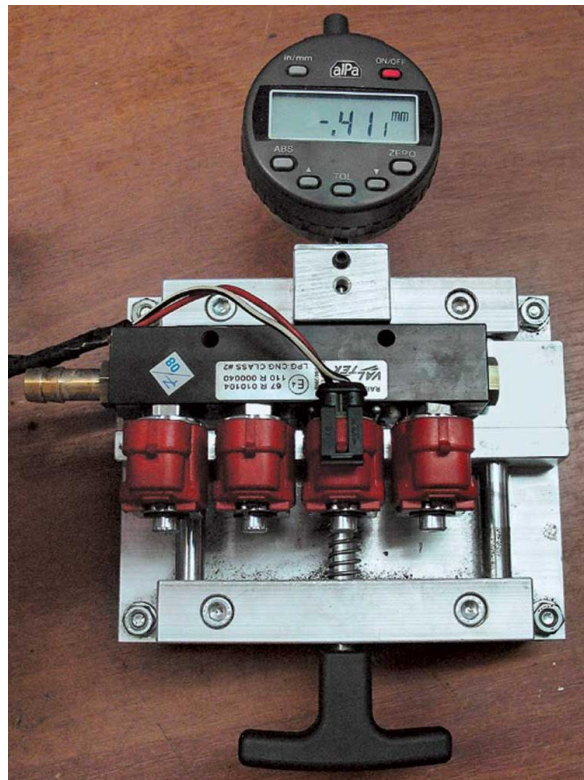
Загальний вигляд пристрою для перевірки та калібрування форсунок.
